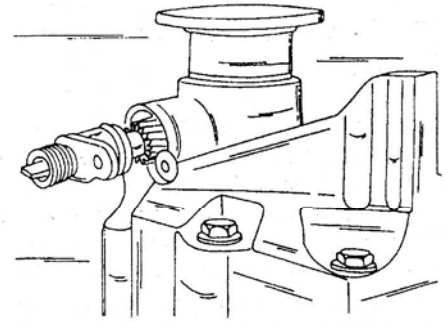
Трубка спидометра расположена в задней крышке коробки передач.
